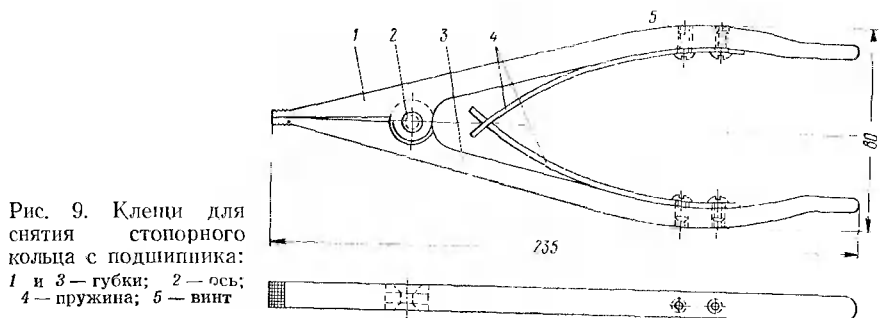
Клещи для снятия стопорного кольца с подшипника:
